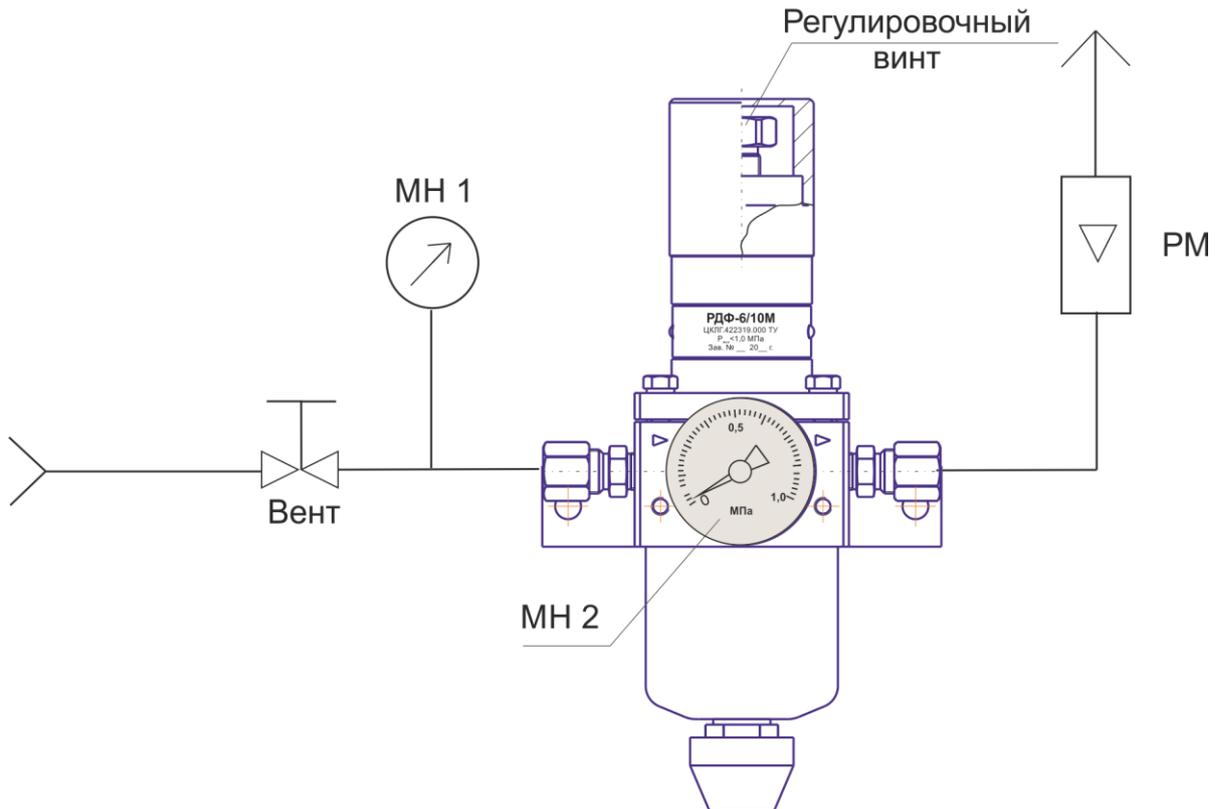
Схема проверки редуктора РДФ-6/10М
